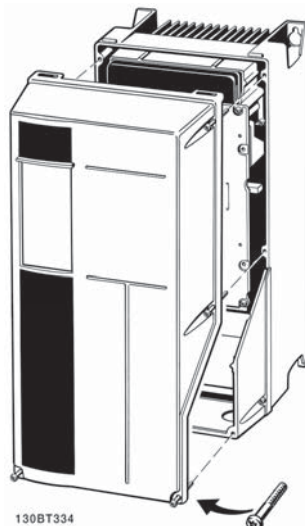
Acceso al cableado de control de las protecciones A4, A5, B1, B2, C1 y C2
